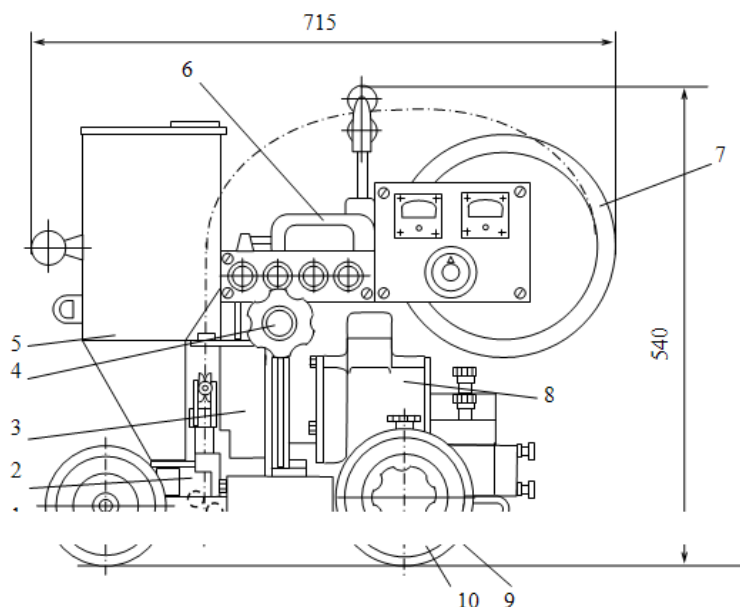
Общий вид автомата АДФ-1002УЗ: 1 – шасси переднее; 2 – мундштуки; 3 – механизм подачи электродной проволоки (сварочная головка); 4 – маховичок корректировочного механизма; 5 – бункер для флюса основной; 6 – кронштейн с пультом управления; 7 – кассета
